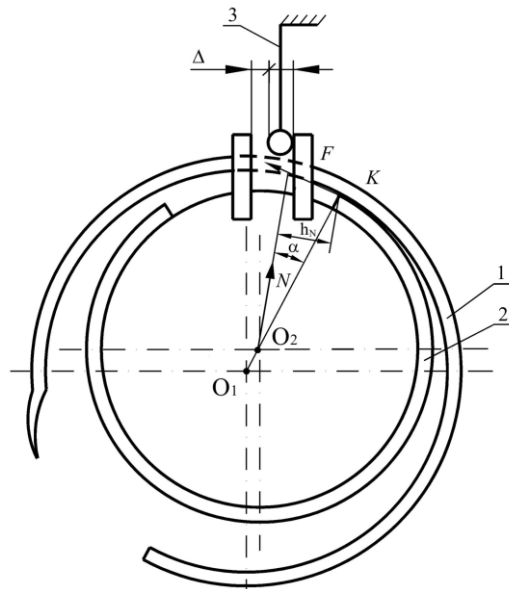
Схема поворачивания шпулдержателя против движения швейного крюка: 1 – швейный крюк; 2 – шпулдержатель; 3 – установочный палец
